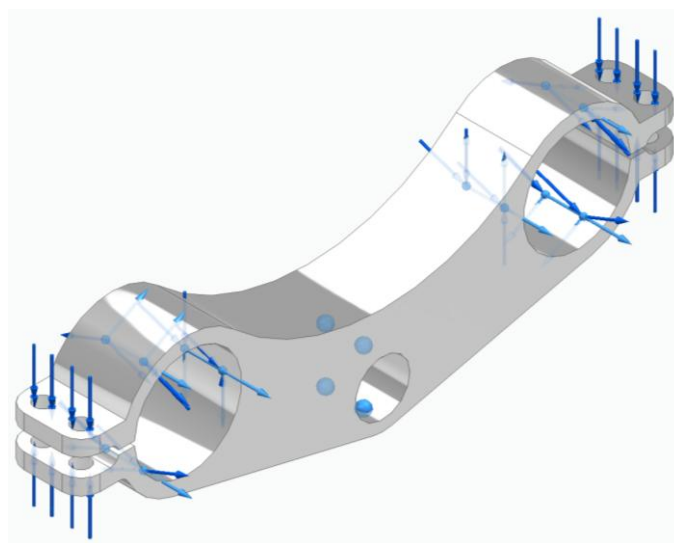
Fuerzas y restricciones aplicadas sobre la tija. (fuente: propia)
